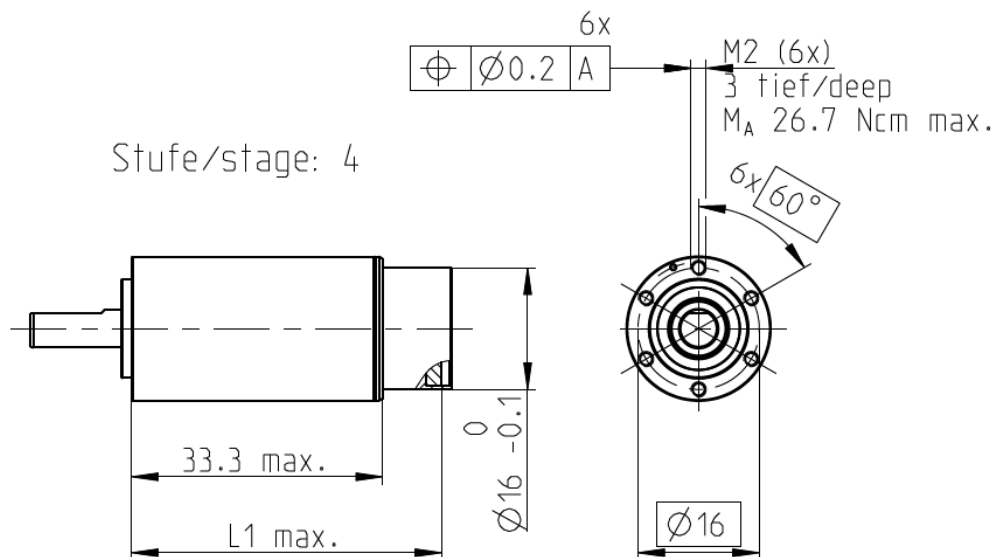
Medida de los tornillos que fijarán la reductora a la pieza. [46]
